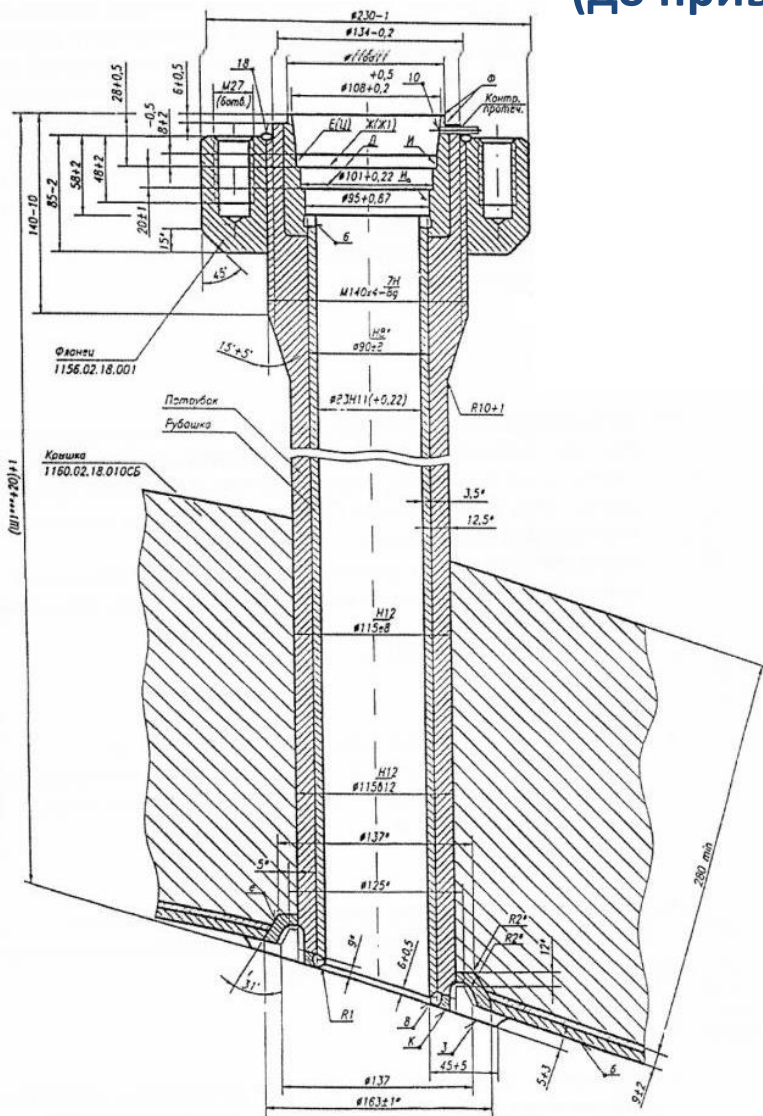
Узел приварки патрубков СУЗ к крышке ВБ установки В-320 (серийные блоки ВВЭР-1000)
